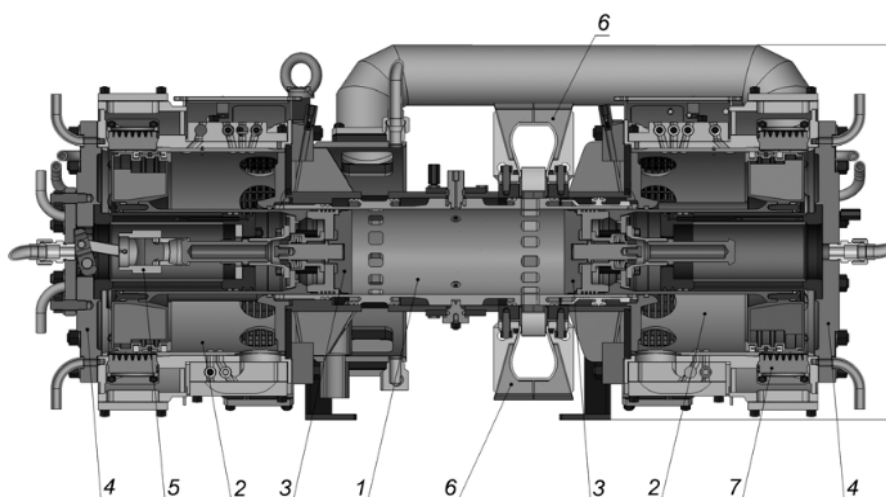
Свободнорпоршневой двигатель 1МП120:
